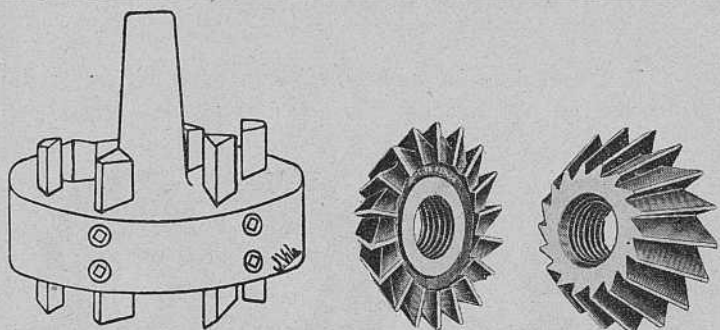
Fresa frontal de dientes postizos. Figs. 680 y 631.—Fresas cortantes por dos caras.
